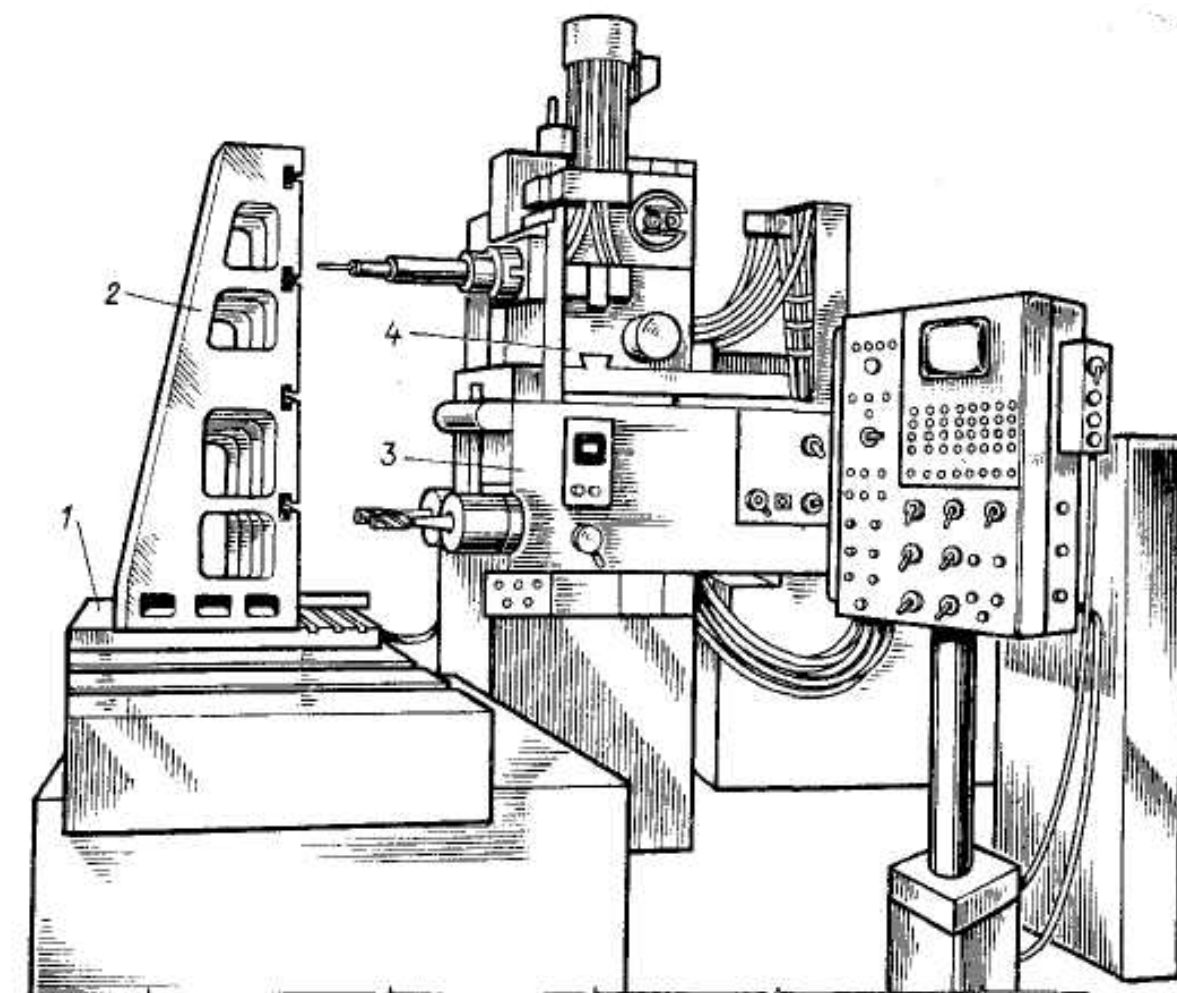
Внешний вид копирующе-фрезерного станка мод. ЛР397Ф3: 1 – стол; 2 – стойка; 3 – шпиндельная бабка; 4 – трехкоординатное измерительно-управляющее устройство
